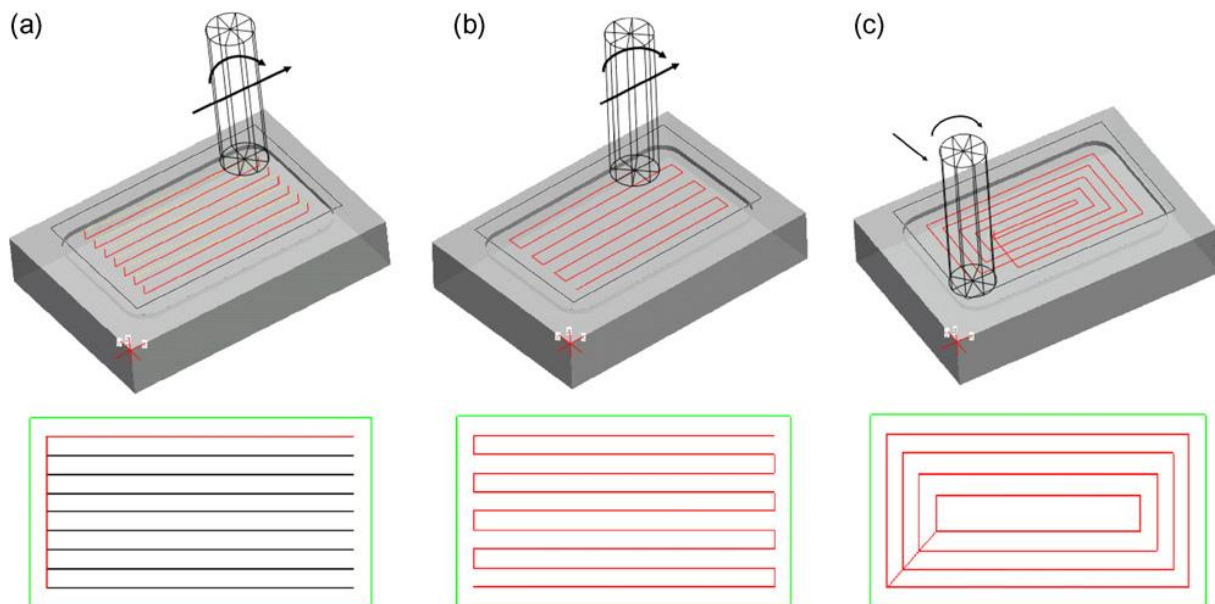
Caminhos de usinagem: (a) *OneWay*; (b) *ZigZag*; e (c) *Parallel Spiral* [28].
